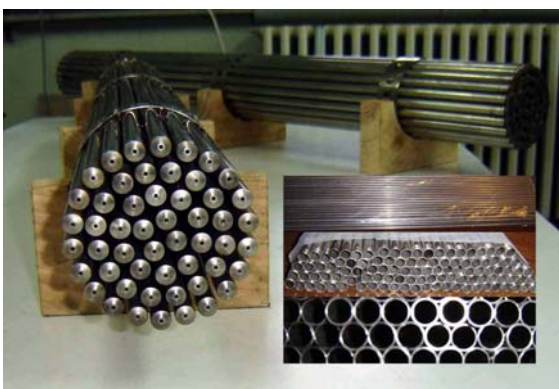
Vista del extremo del EC CARA sin grilla desmontables.
